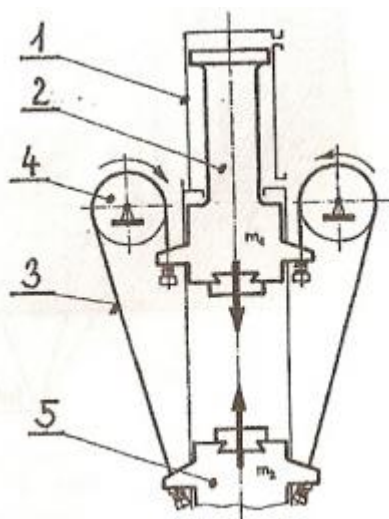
Buchar pro zápustkové kování firmy LASCO [5]
